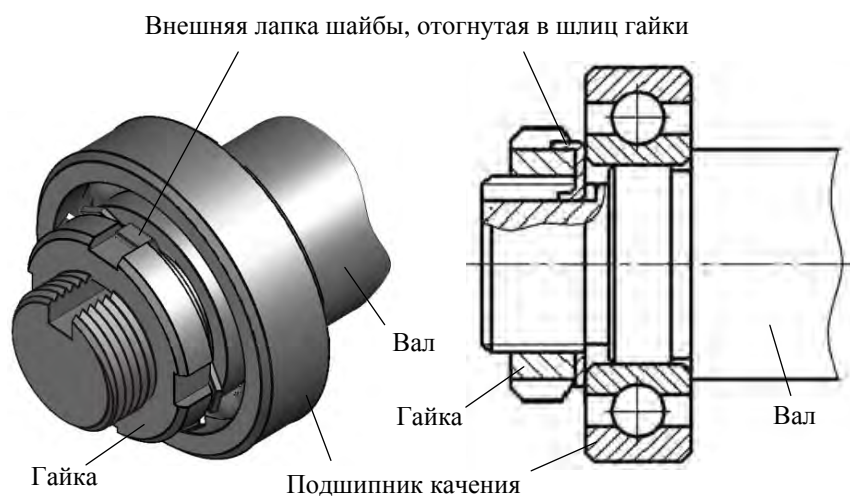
Крепление подшипника на цапфе вала посредством круглой шлицевой гайки (справа чертеж соединения)
